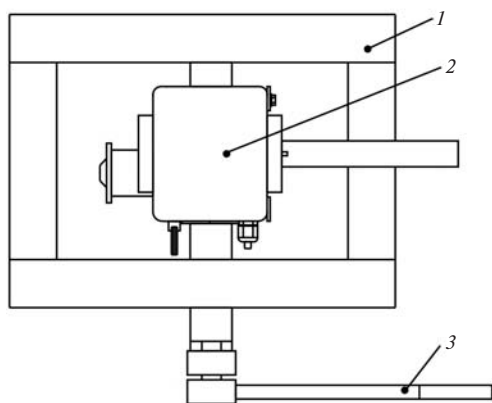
Схема стенда для проведения испытаний на прочность от поворотного усилия: 1 – металлоконструкция поворотной трубы; 2 – испытуемое устройство; 3 – динамометрический ключ
